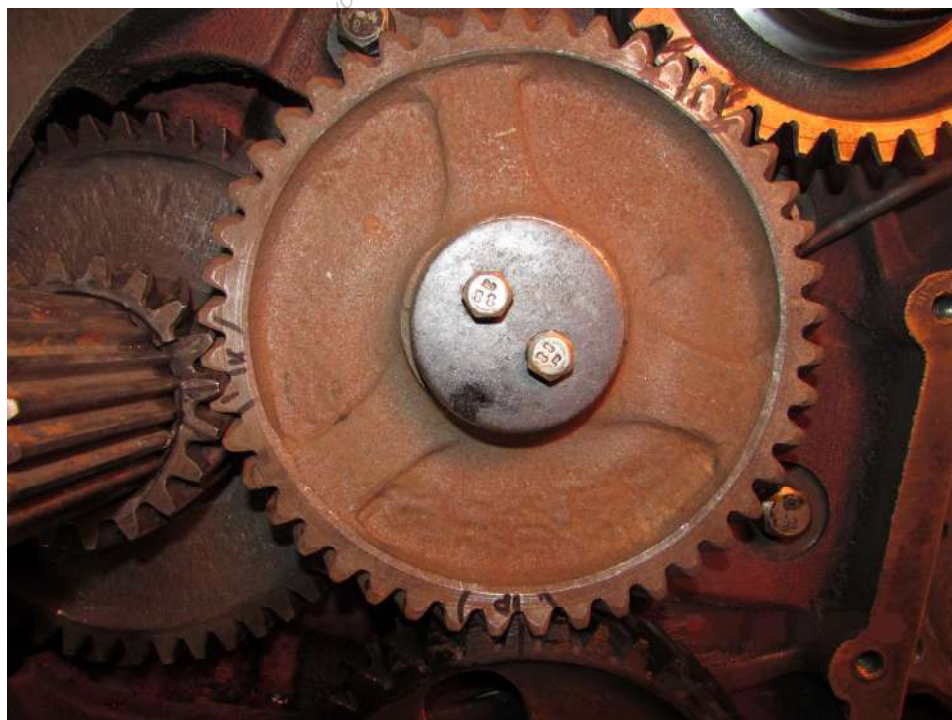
Пример для Зубчатая передача: одно колесо заставляет двигаться другое колесо
